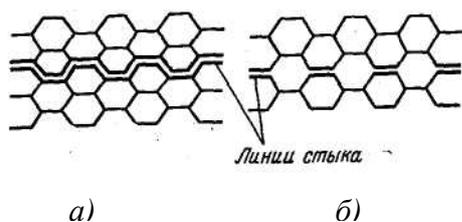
Виды стыка заготовок сотонаполнителя: а – ячейка в ячейку; б – по выступающим граням
